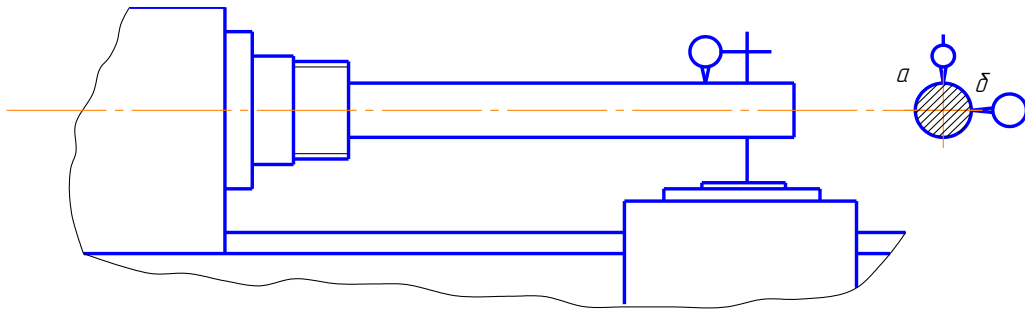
Схема установки индикатора для проверки параллельности оси шпинделя направлению продольного перемещения суппорта
